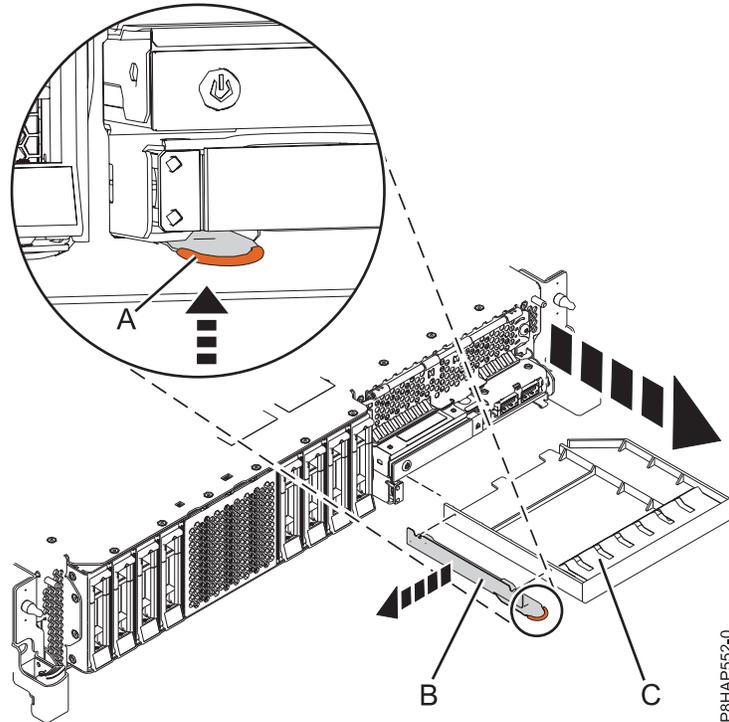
Remova a placa de preenchimento do dispositivo de suporte e o suporte de fixação do sistema.
